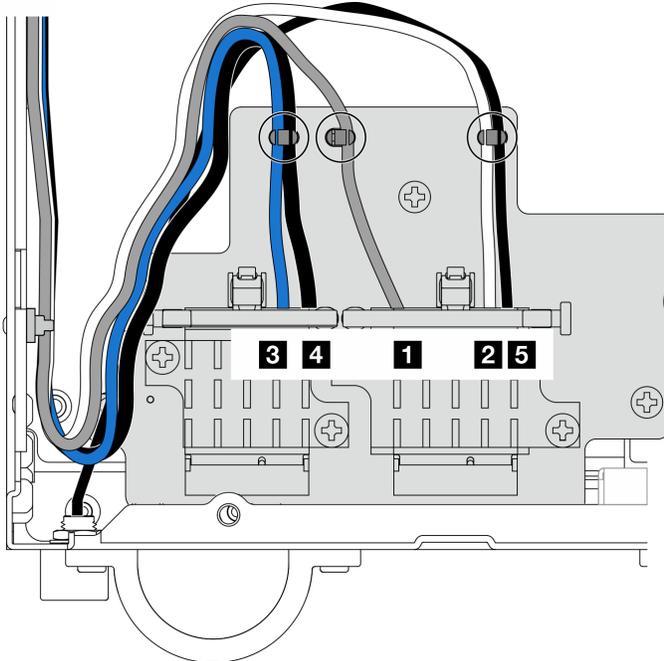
Disposición de los cables de la antena WLAN y Bluetooth
